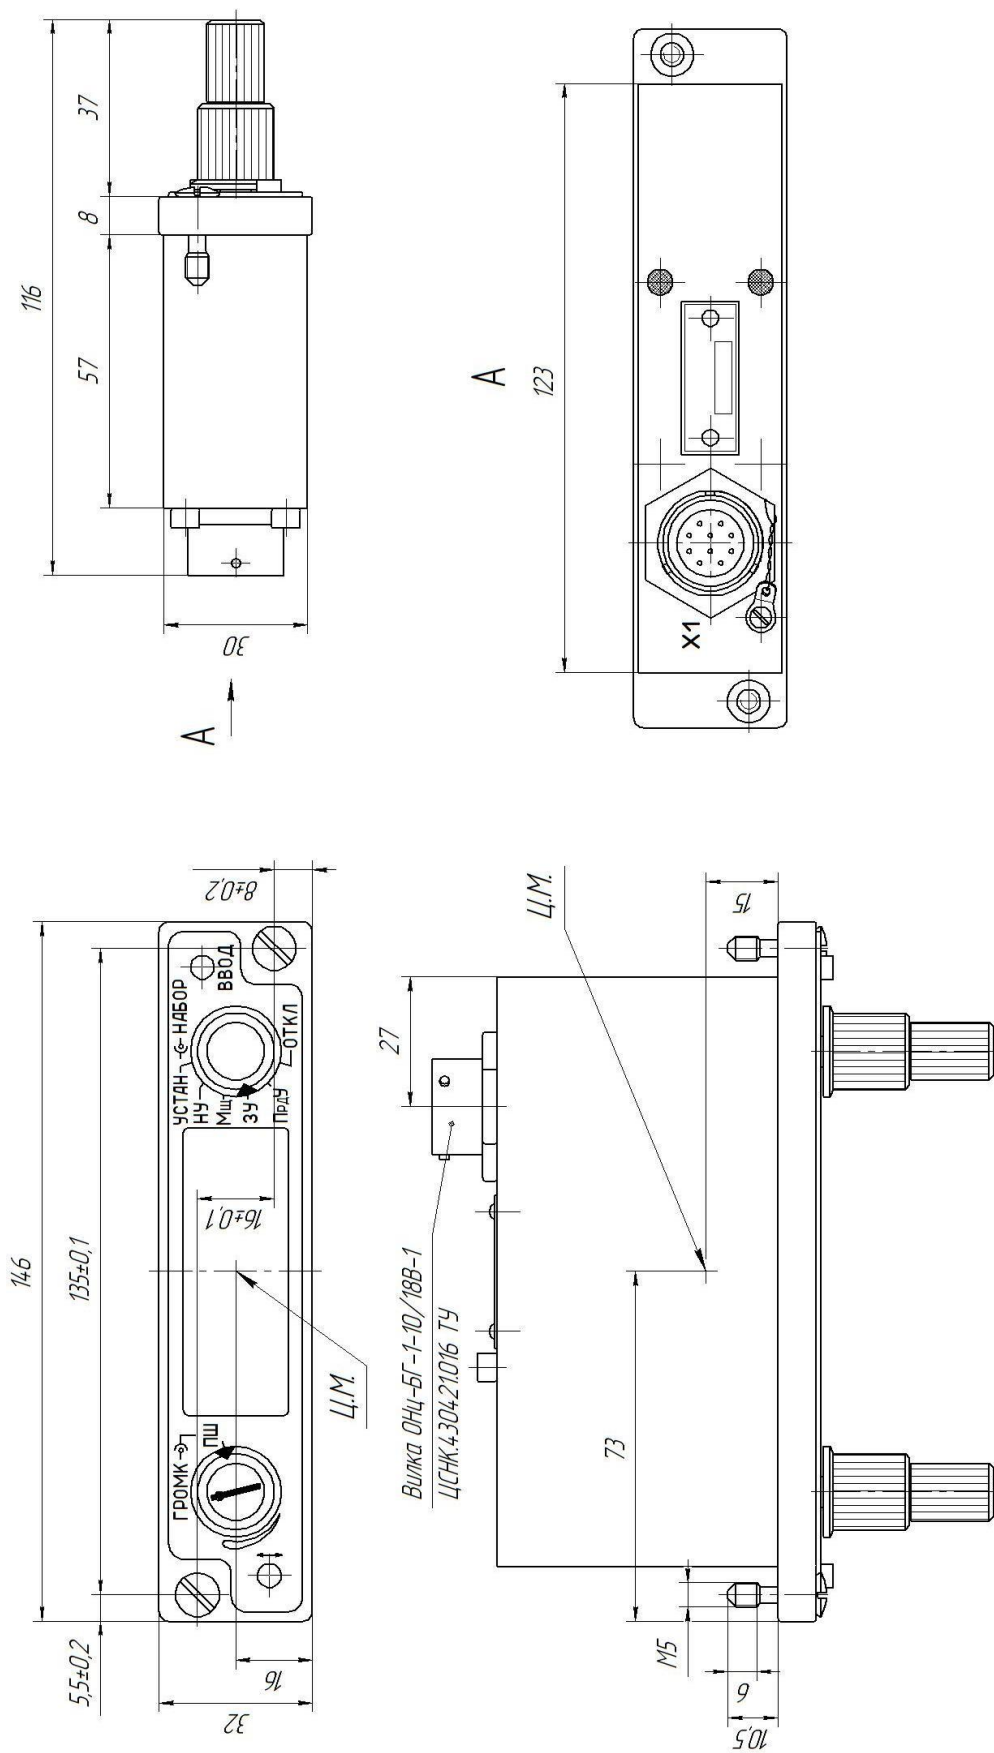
Габаритный чертёж блока Б7П1-Прк
